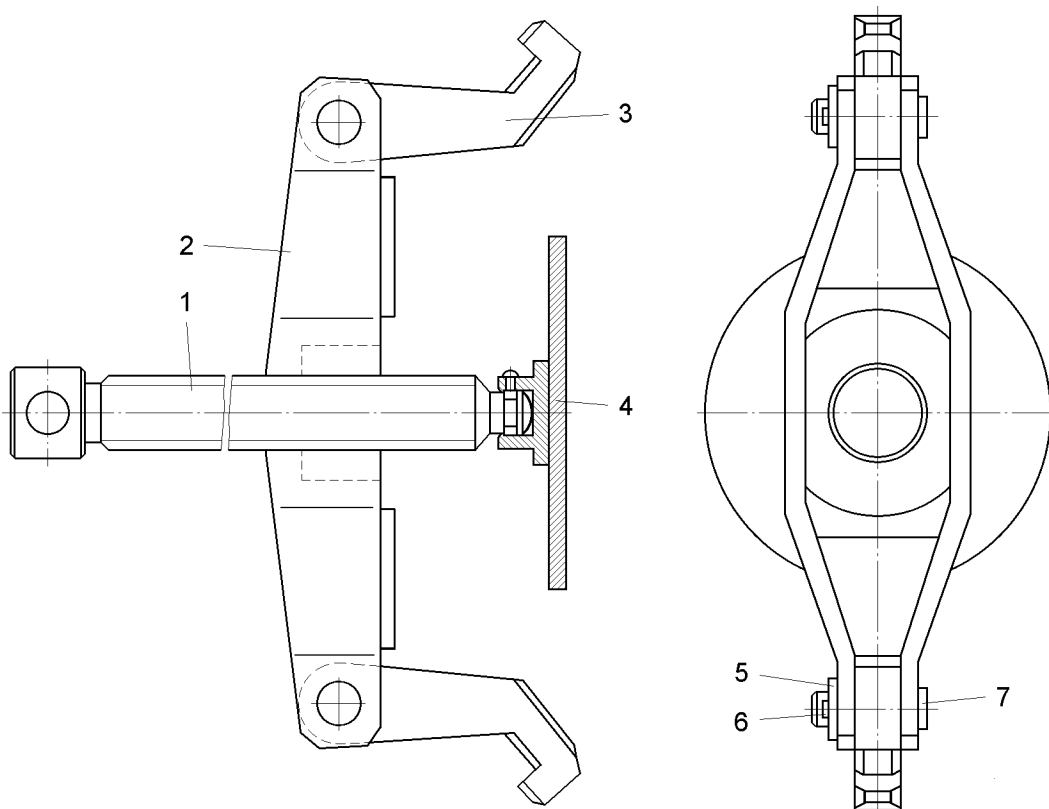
Приспособление-съемник для снятия с коронной шестерни с кожухом:
